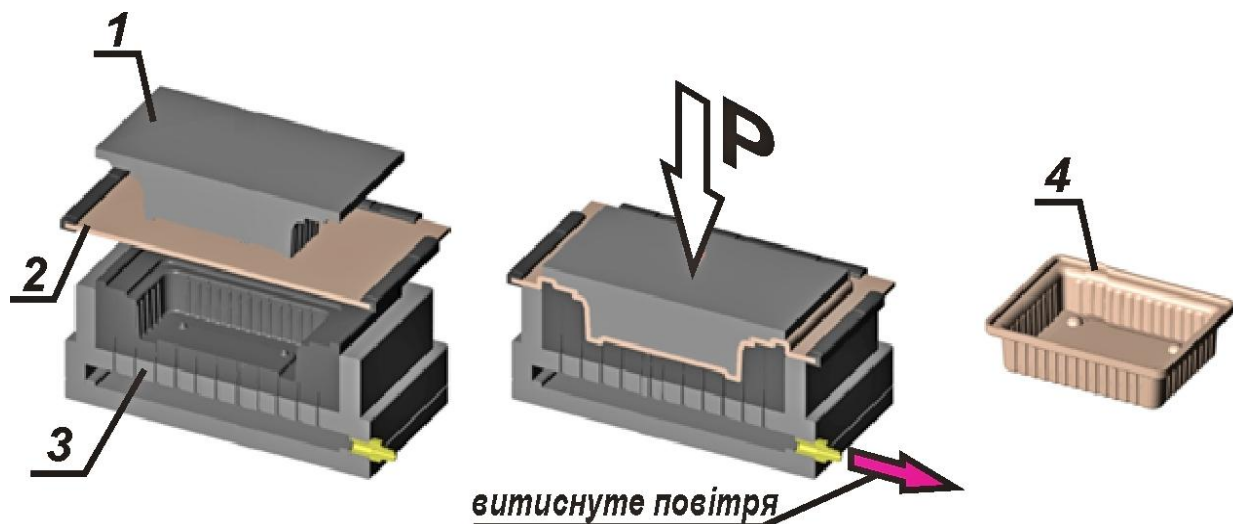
Схема штамування заготовок з листових пластмас:
